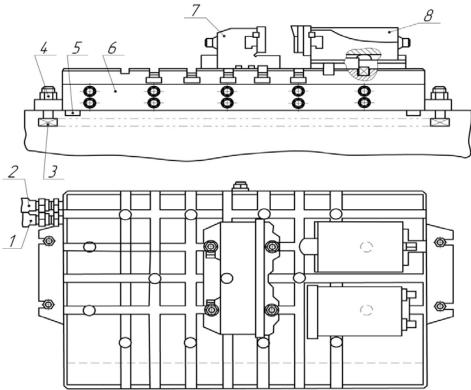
Универсально-наладочное приспособление для установки плоских деталей: 1, 2 — штуцеры; 3 — болт; 4 — гайка; 5 — шпонка; 6 — плита; 7 — неподвижная губка; 8 — подвижная губка
